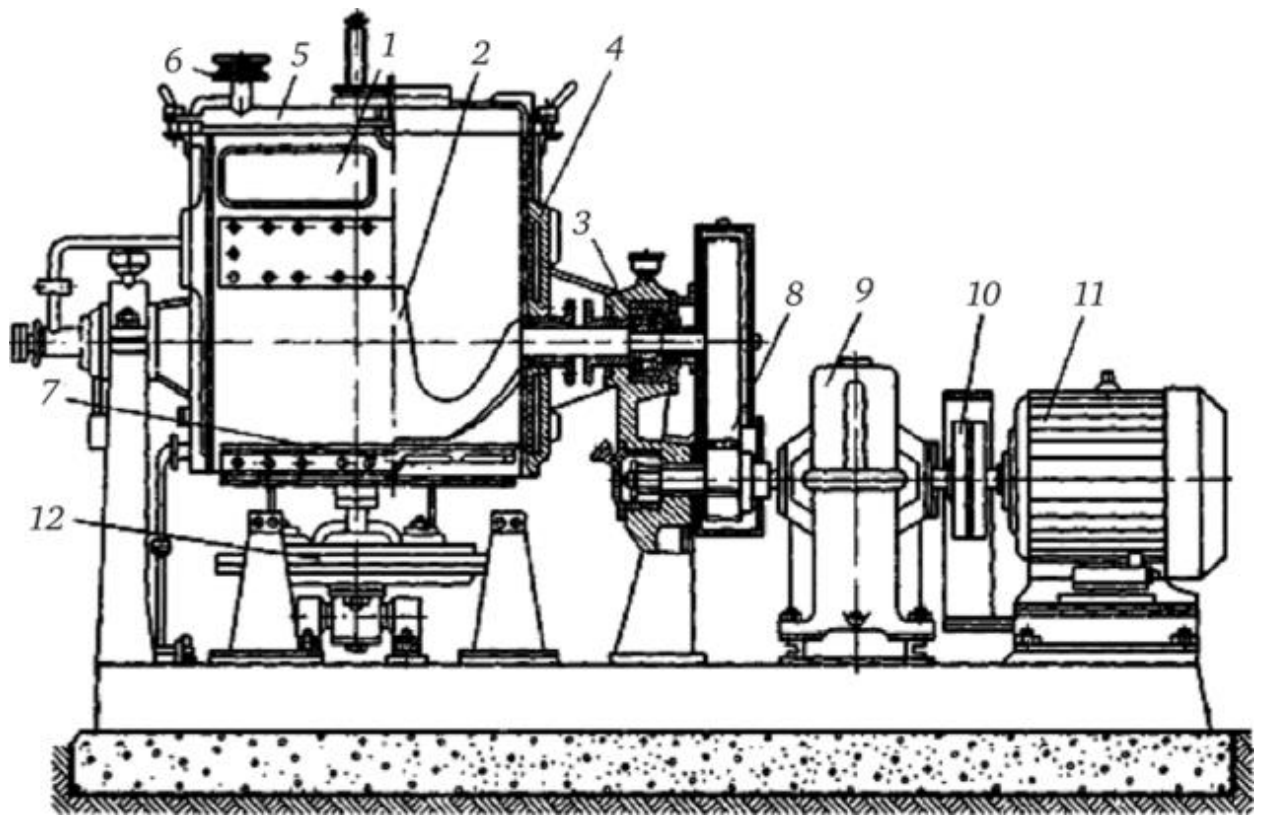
Схема двоходового змішувача з Z-подібними лопатями
